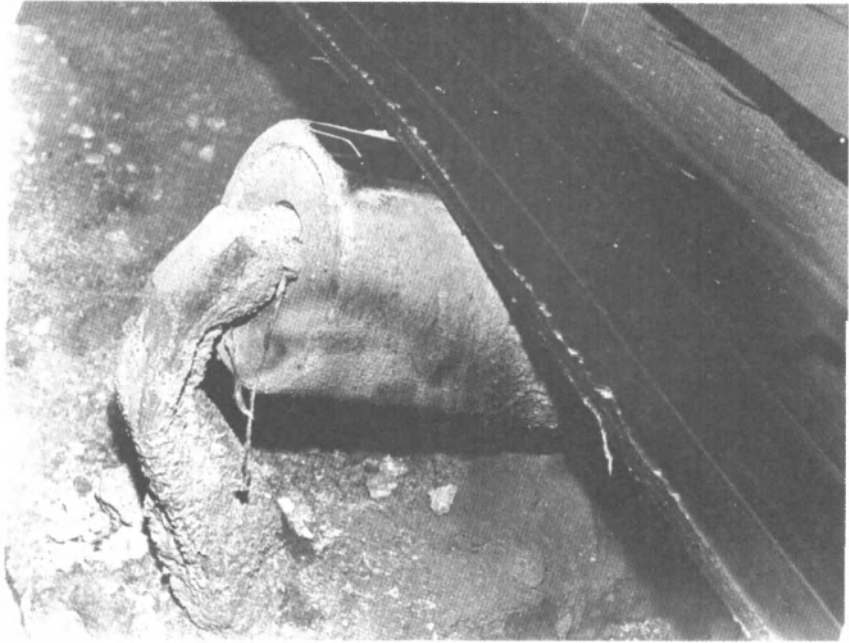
Опорно-центрирующий подшипниковый узел
